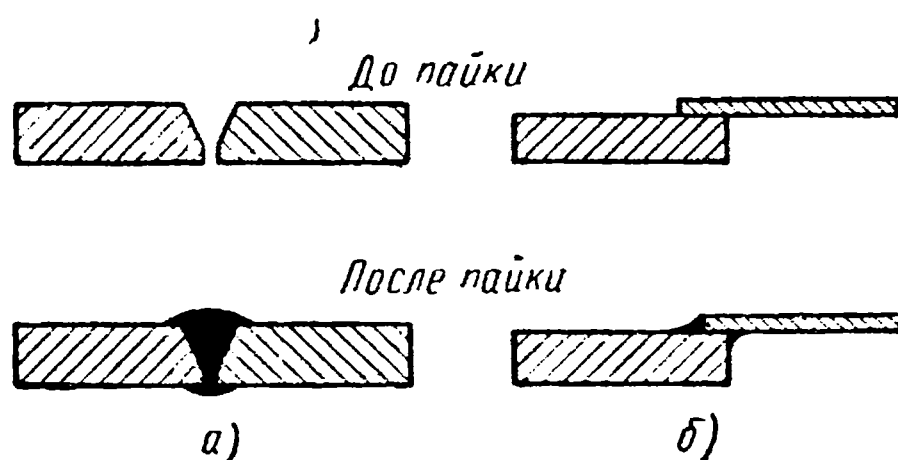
Схема образования шва при пайке-сварке:
